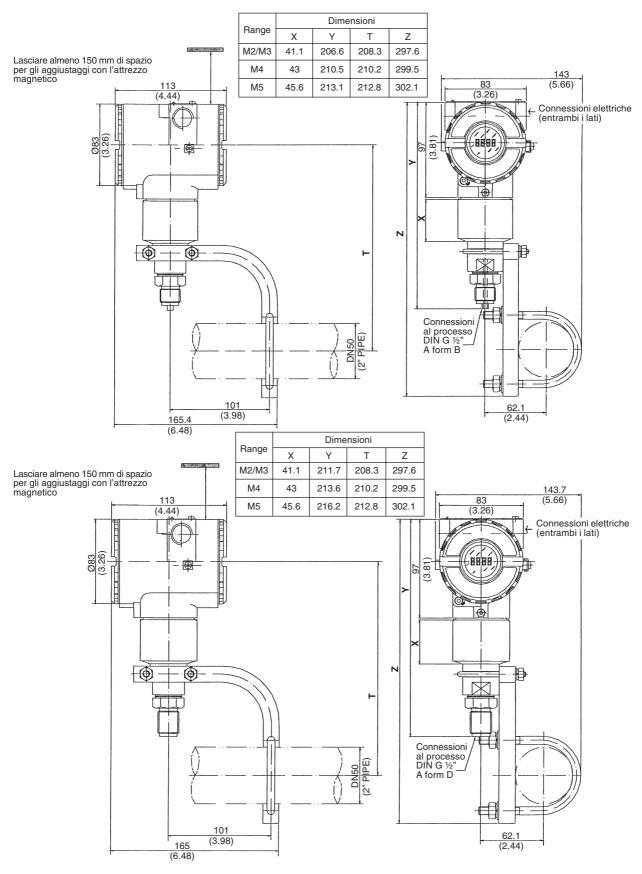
B - Dimensioni di ingombro e posizioni di montaggio per il trasmettitore LD291.
